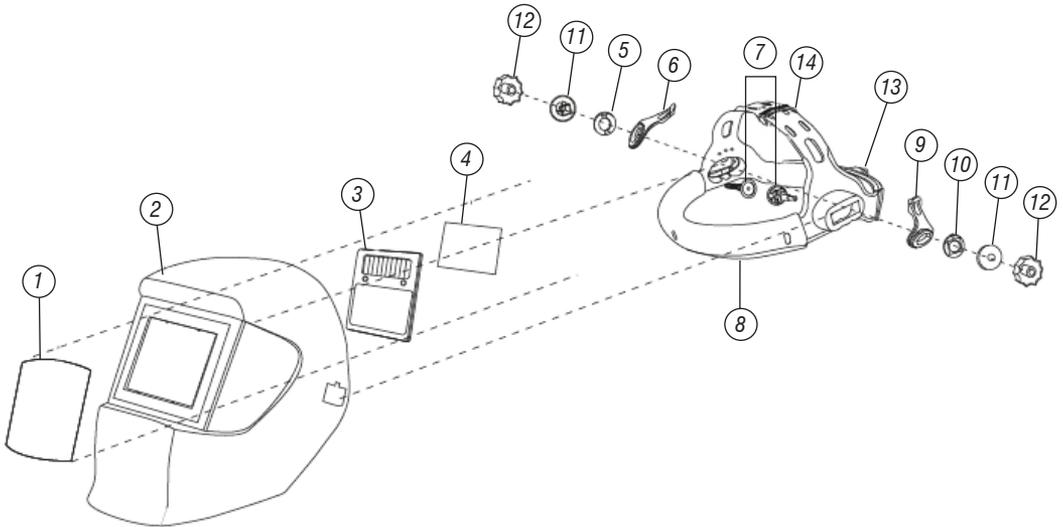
Componentes de la Máscara Fotosensible para soldar
